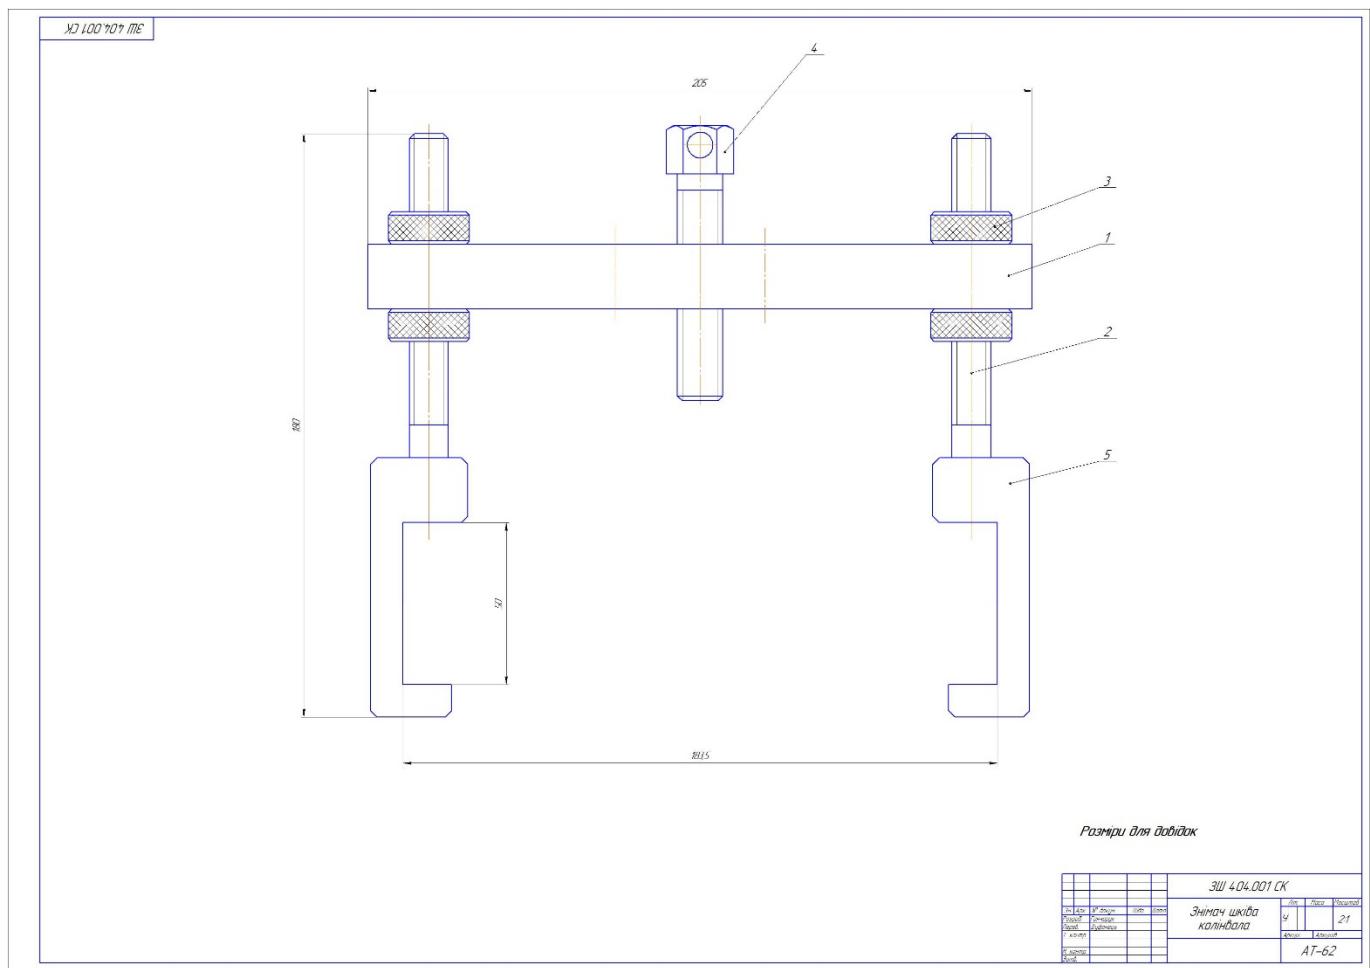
Пристрій ЗШ 404 для знімання шківа колінвала складальне креслення.
